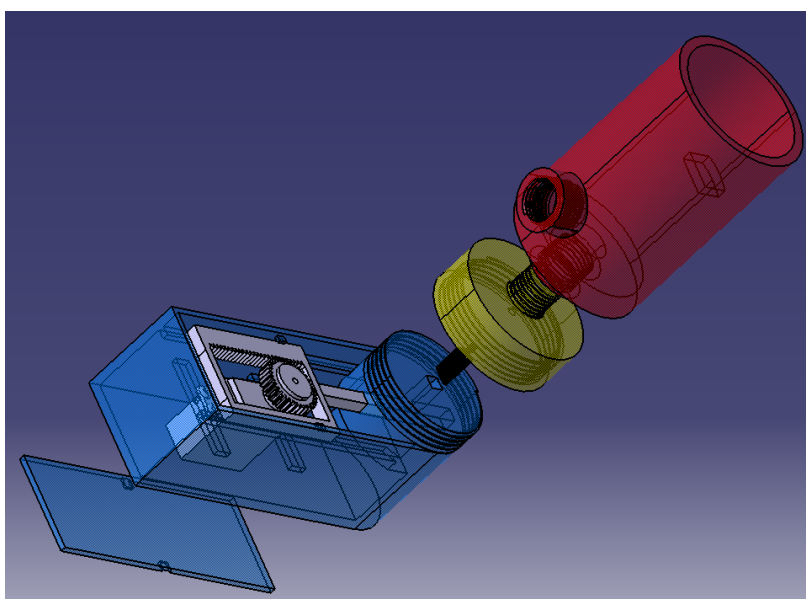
Visão frontal do CAD projetado para a válvula de PLA.
